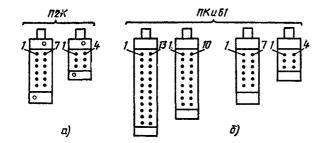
Расположение контактов переключателей; а — типа П2К; 6 — типа ПКи61
